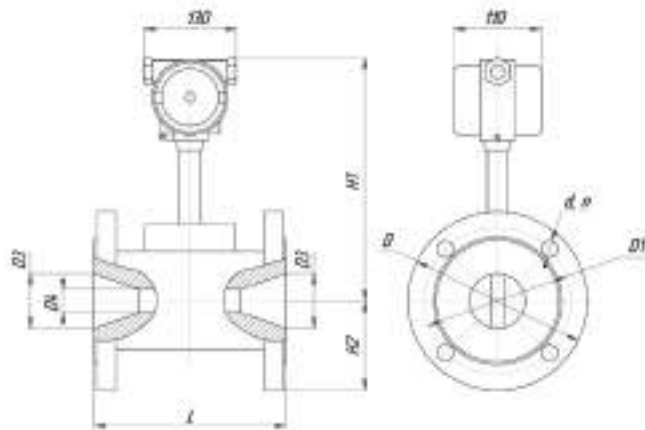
Габаритные и присоединительные размеры для преобразователя расхода Тирэс (исполнение H) со встроенным струевыпрямителем
